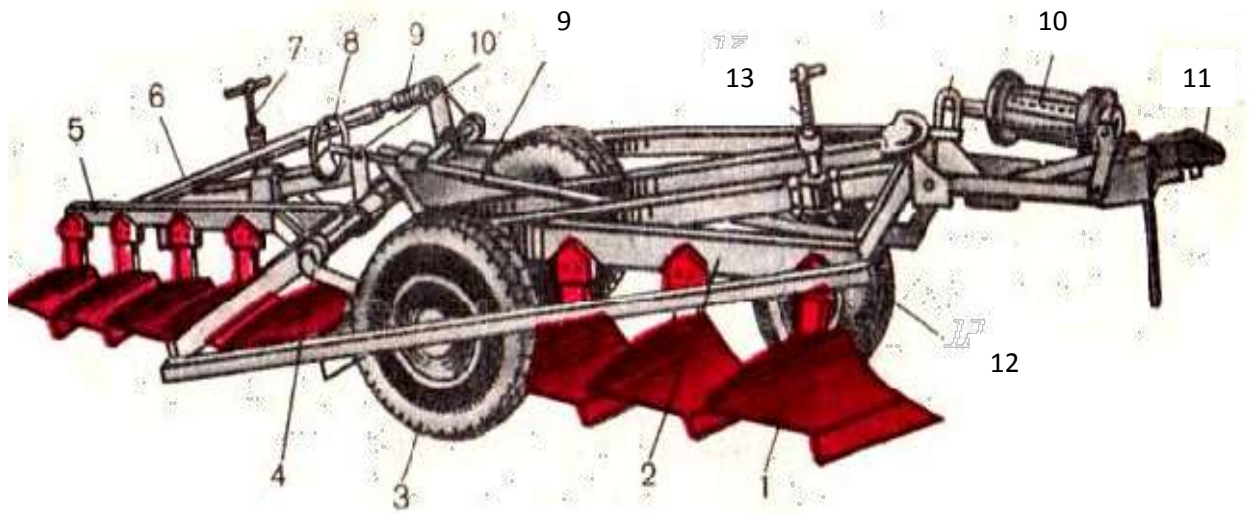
Лемешковый плуг-луцильщик ППЛ-10-25: 1 – корпус; 2 и 5 – секции рамы; 3 и 12 – колеса; 4 – ось; 6 – штанга; 7 и 13 – регуляторы глубины; 8 – штурвал; 9 – тяга; 10 – гидроцилиндр; 11 – прицепное устройство.
